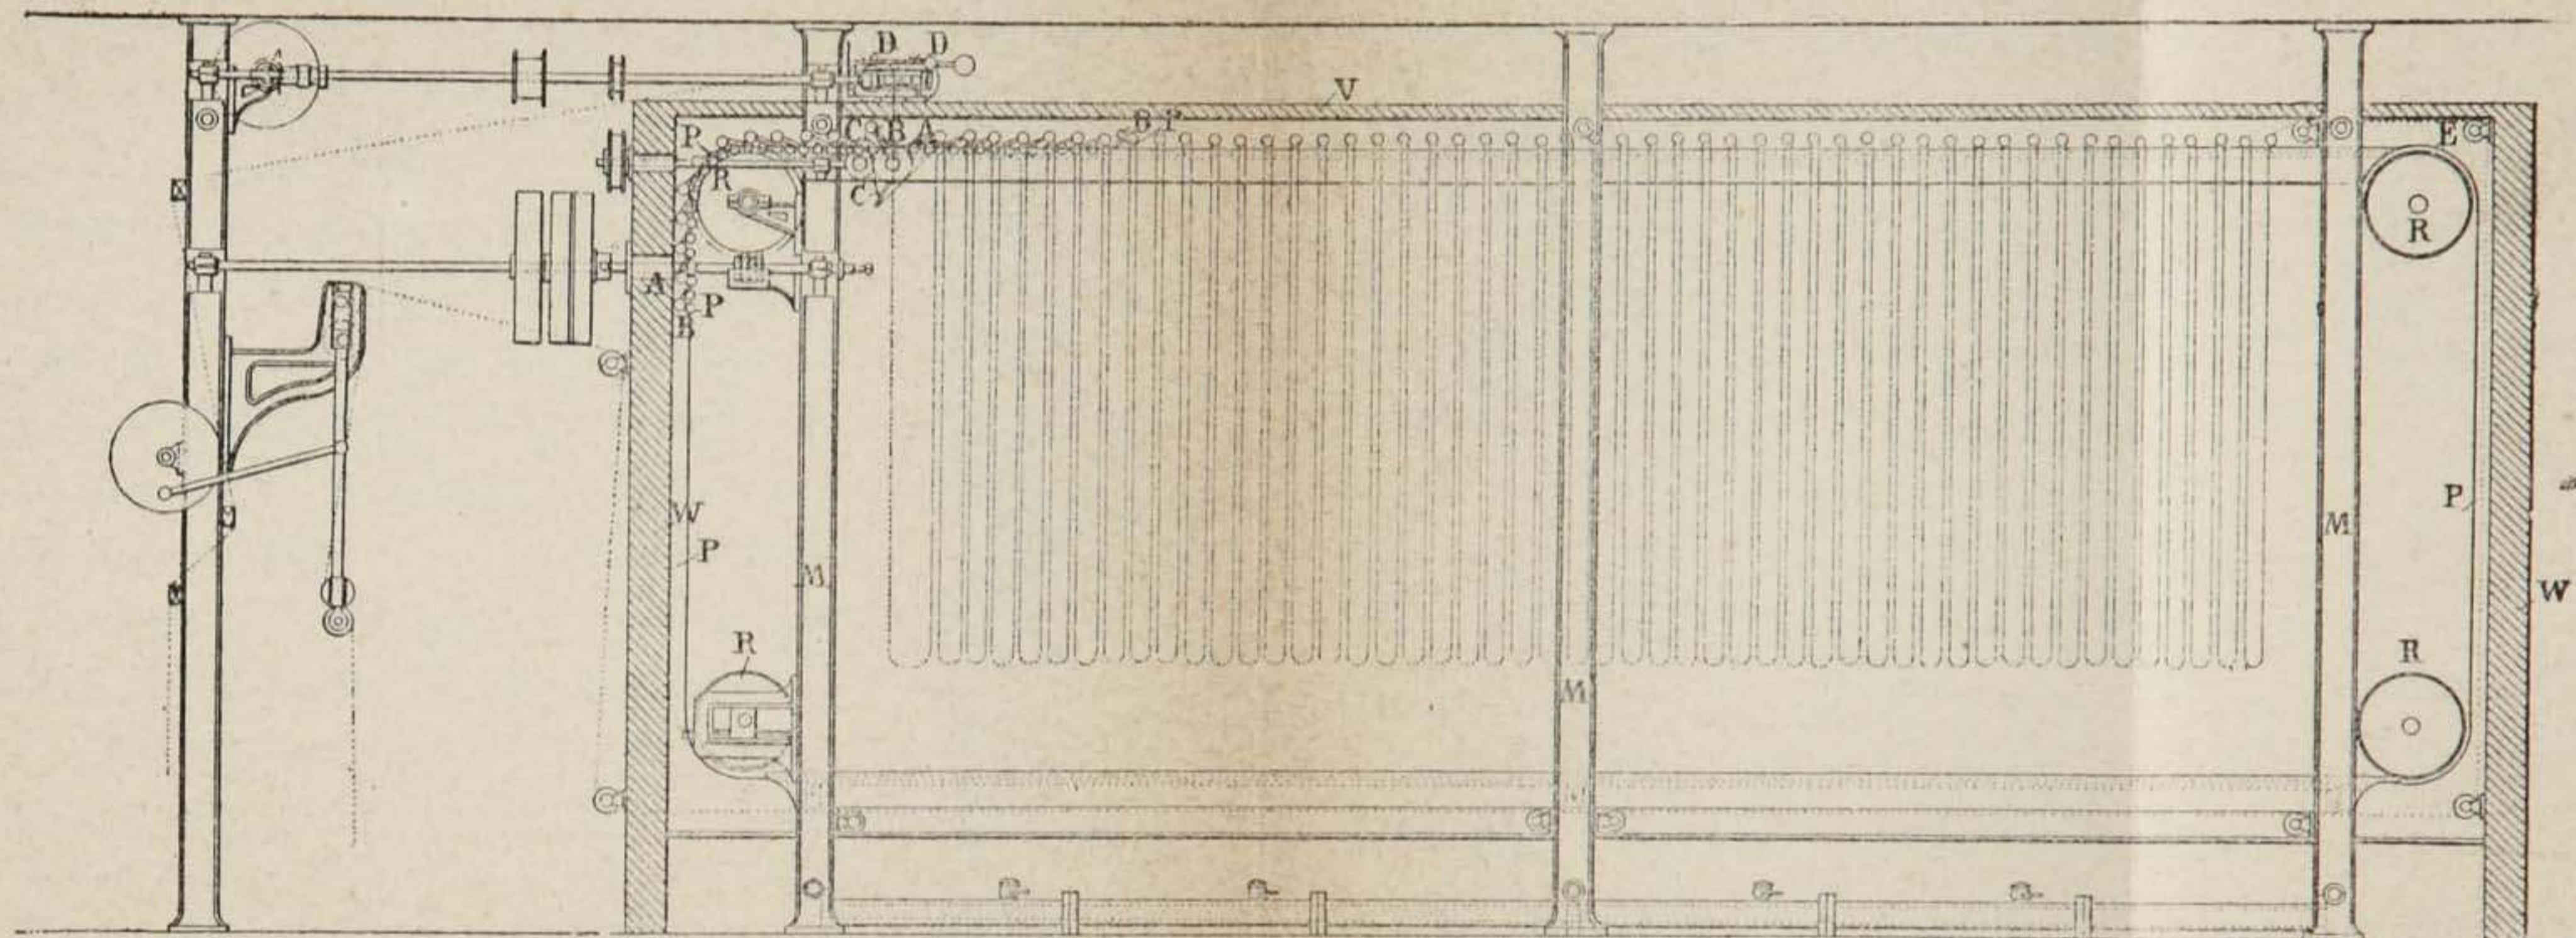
Machine à vaporiser système continu REMY. — Face.
